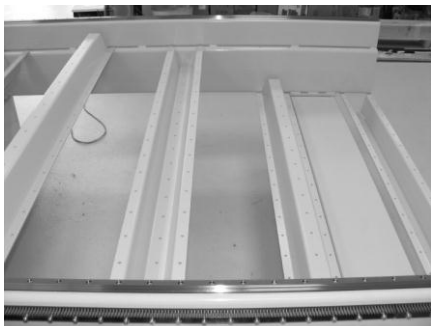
Tischauflageverstreben auf vier Höhen montierbar
